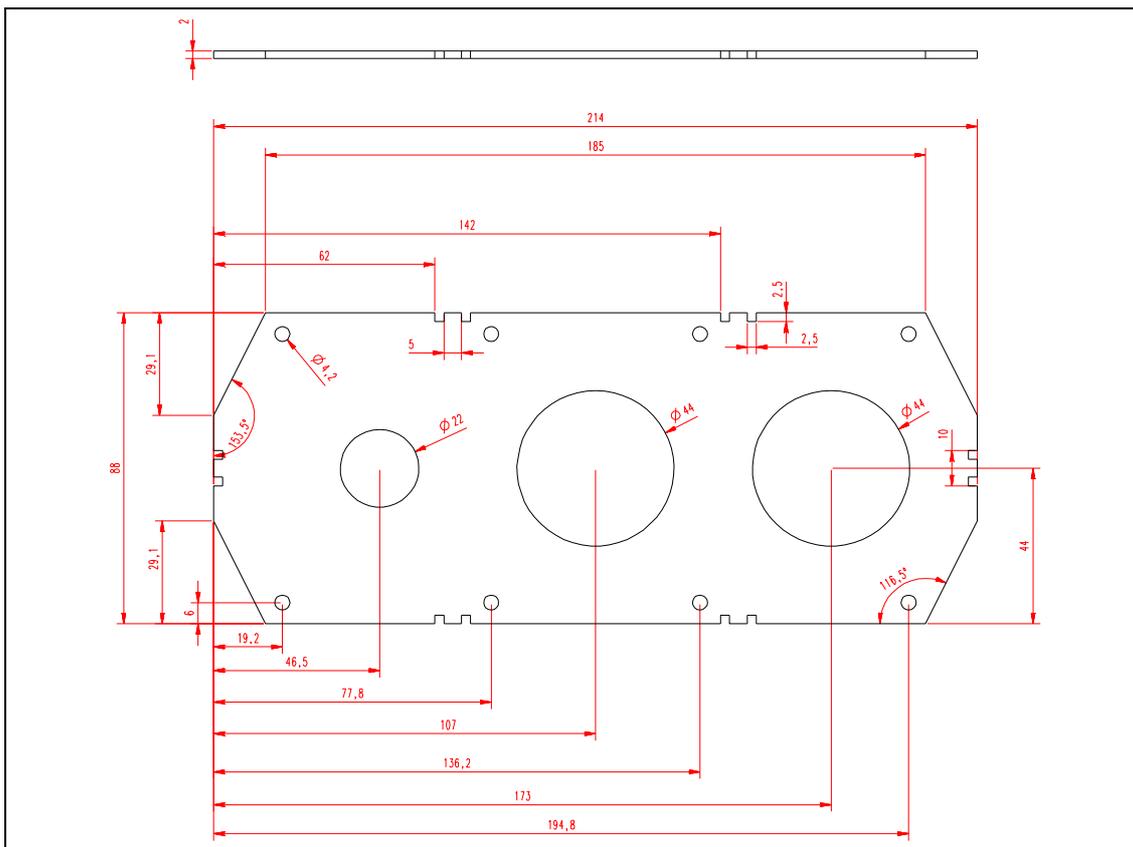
Plaque d'entrée de câble, installation MM6 UL.
